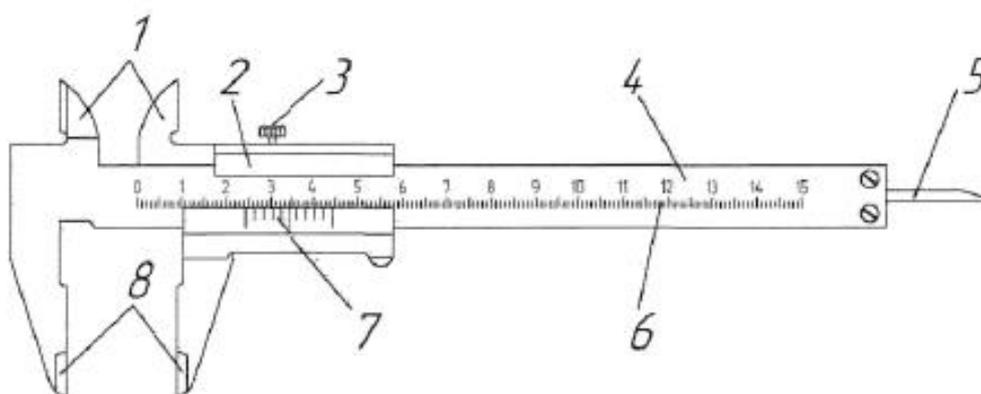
Штангенциркуль ШЦ I двухсторонний с глубиномером
